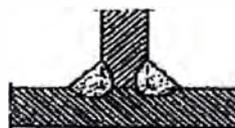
Junta de filete con soldadura de ambos lados
